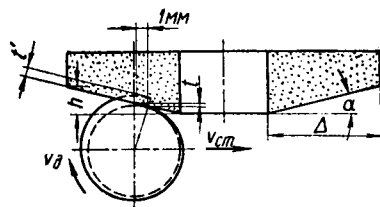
Схема расположения шлифовального круга и детали при обдирке цилиндрической поверхности торцом круга.
